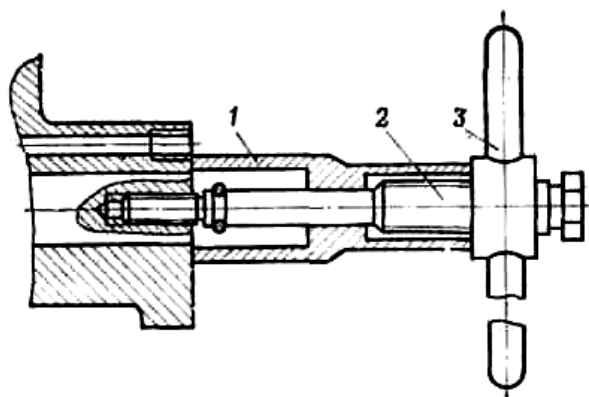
Знімач вісі блока шестерень заднього ходу И-801.32.000: 1 - корпус; 2 - гвинт; 3 - рукоятка
